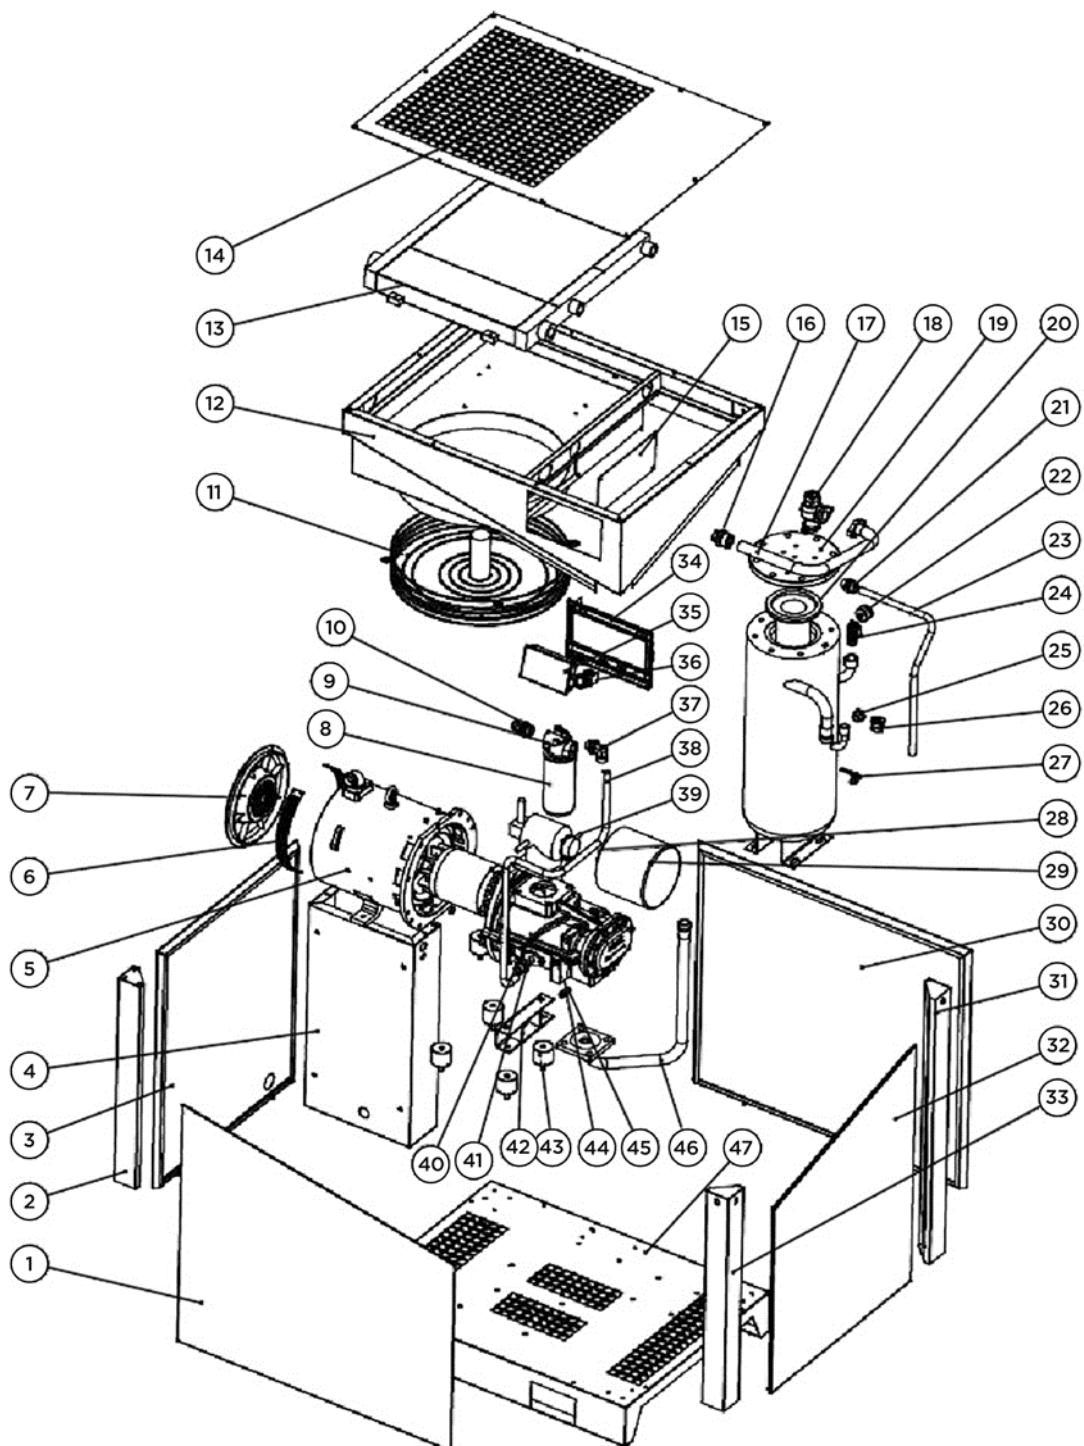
Деталировка на винтовой компрессор с прямым приводом серии IC 7,5-50 D
